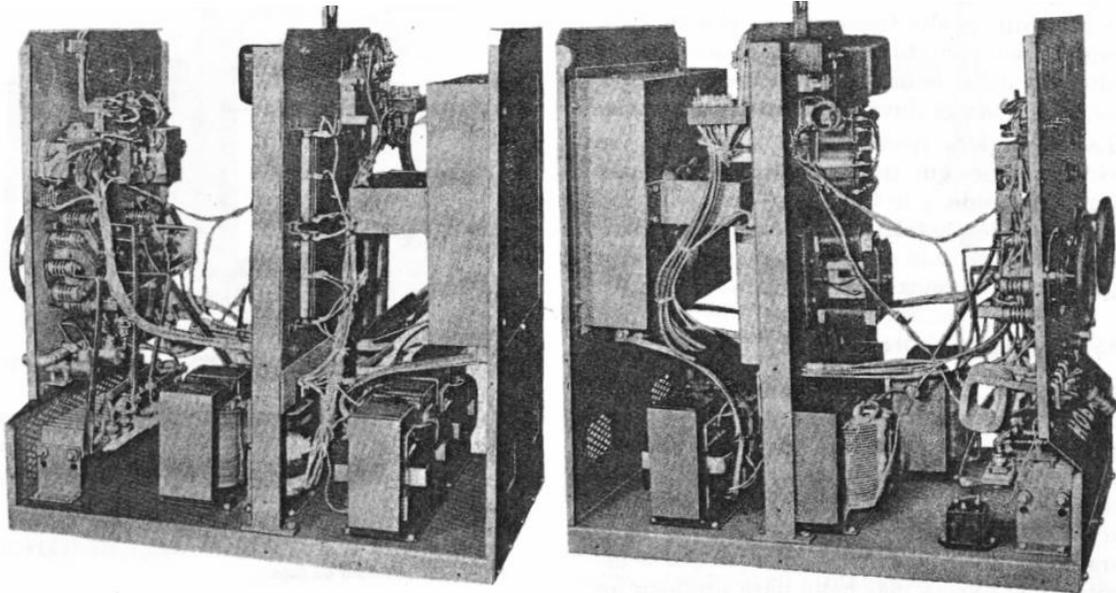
Vistas derecha e izquierda del interior de una máquina T.I.G.
